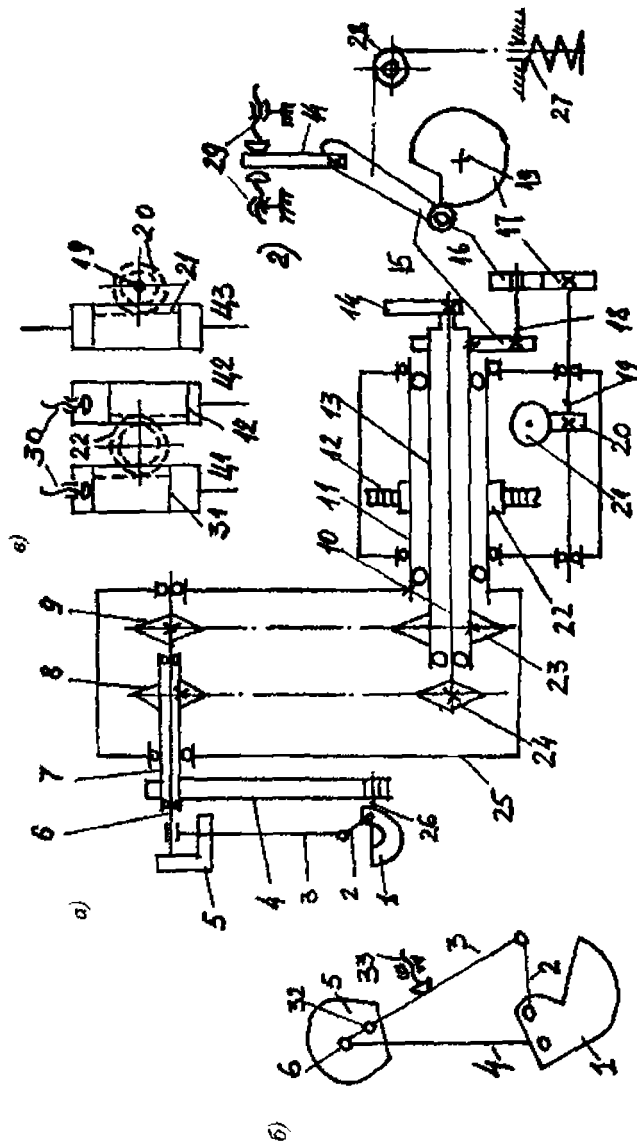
Кинематическая схема манипулятора для заливки металла
